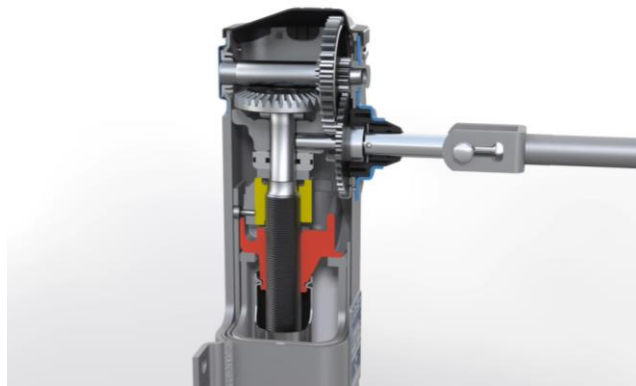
Mecanismo de gato mecánico Fuente: Jost world Chanel/youtube
